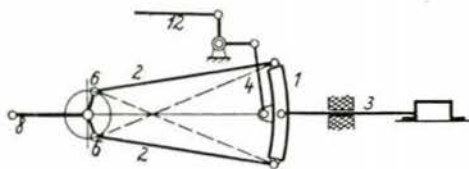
Schemaskizze zu der Stephenson-Steuerung (aus: Henschel-Lokomotiv-Taschenbuch)
